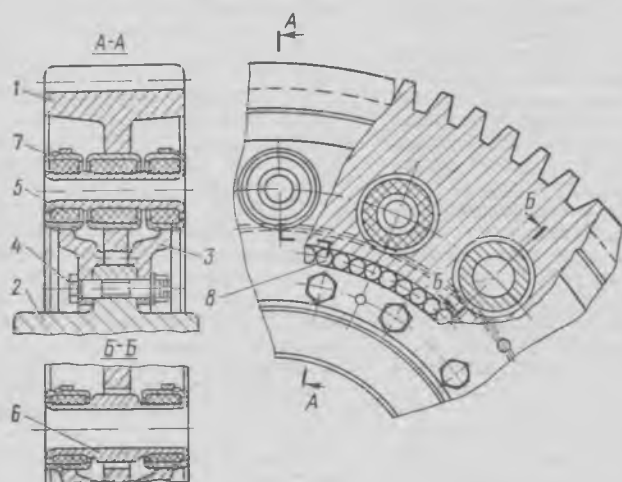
Унифицированное упругое самоустанавливающееся зубчатое колесо конструкции ВНИТИ:
